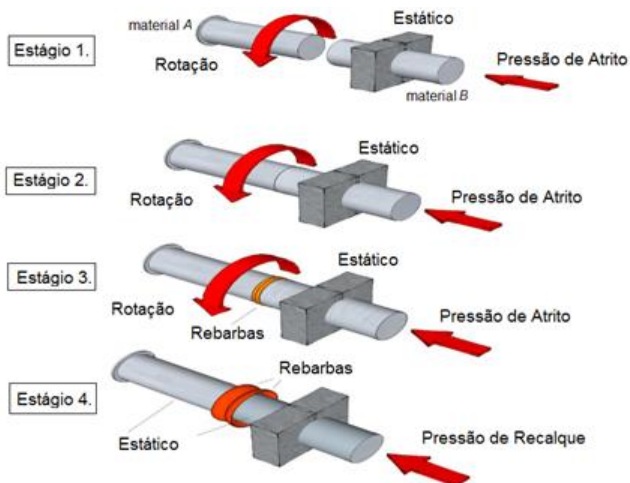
Soldagem por atrito rotativo (Adaptado de KANASHIRO, 2017).
